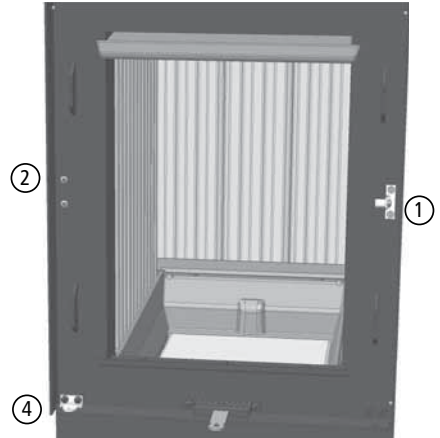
Gerätefront, Verschlussblech und Scharnier
